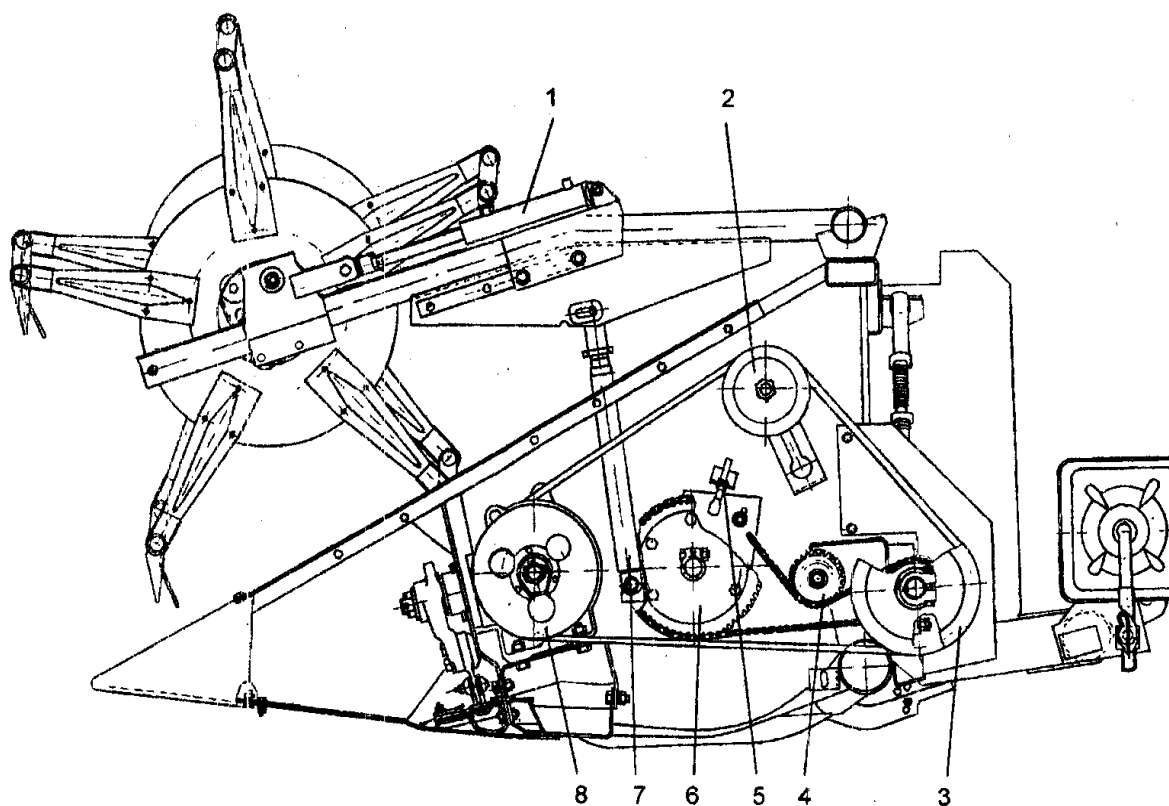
Жатка (левая сторона): 1 – гидроцилиндр выноса мотовила; 2 – натяжной шкив; 3 – шкив контрприводного вала; 4 – натяжная звездочка; 5 – гайка регулировки установки шнека по высоте; 6 – предохранительное устройство; 7 – гидроцилиндр подъема мотовила; 8 – механизм качающейся шайбы
